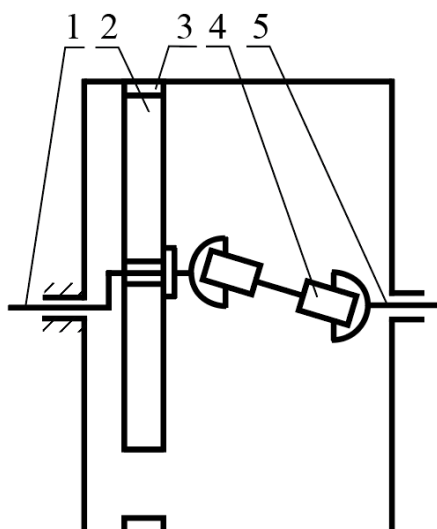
Типичная схема планетарно-цевочного редуктора: 1 – входной вал; 2 – сателлит; 3 – обойма с цевками; 4 – механизм передачи вращения; 5 – выходной вал
